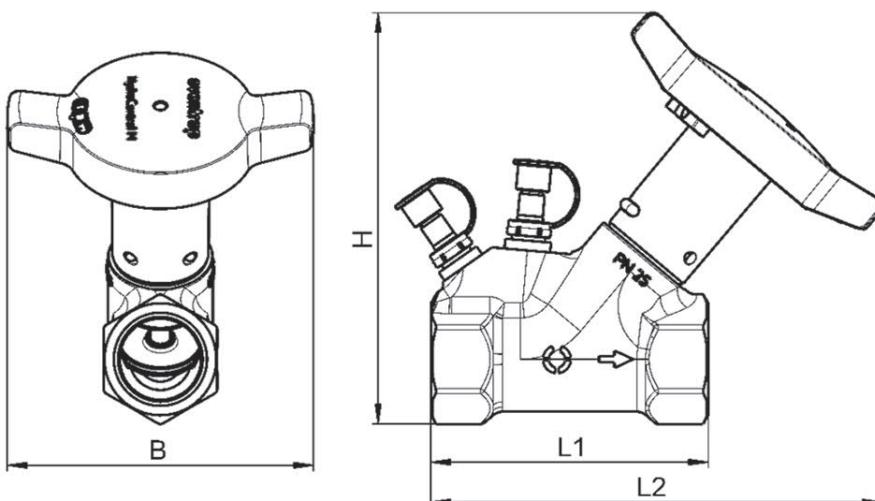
Dimensiones vista lateral / vista frontal rosca interior
